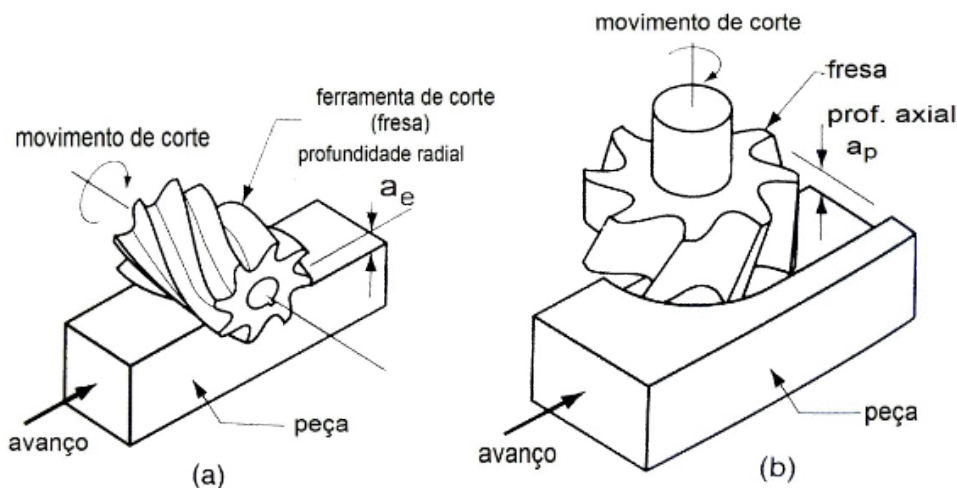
Fresagem Cilíndrica (a); Fresagem Frontal (b) [4]
